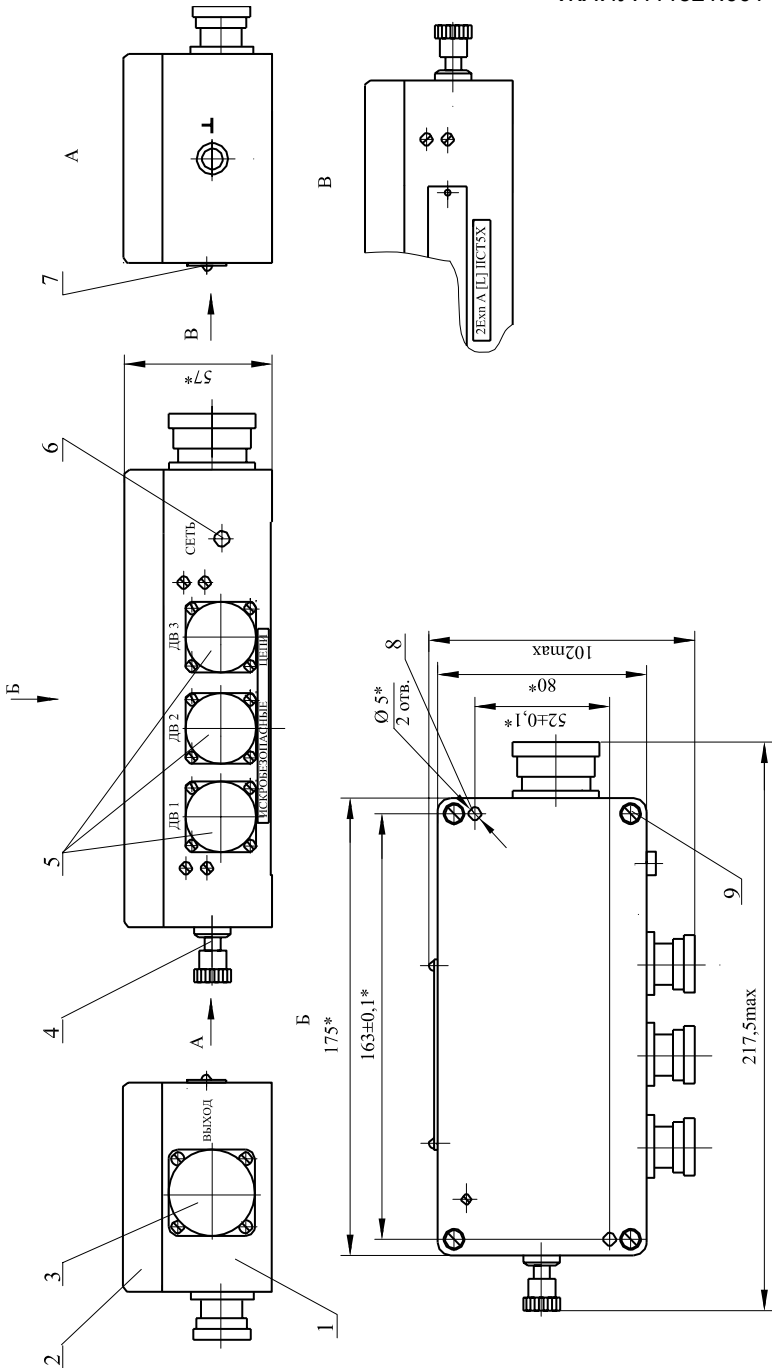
(1 из 2) - Габаритно - установочные размеры согласующего блока БС-16-18В
